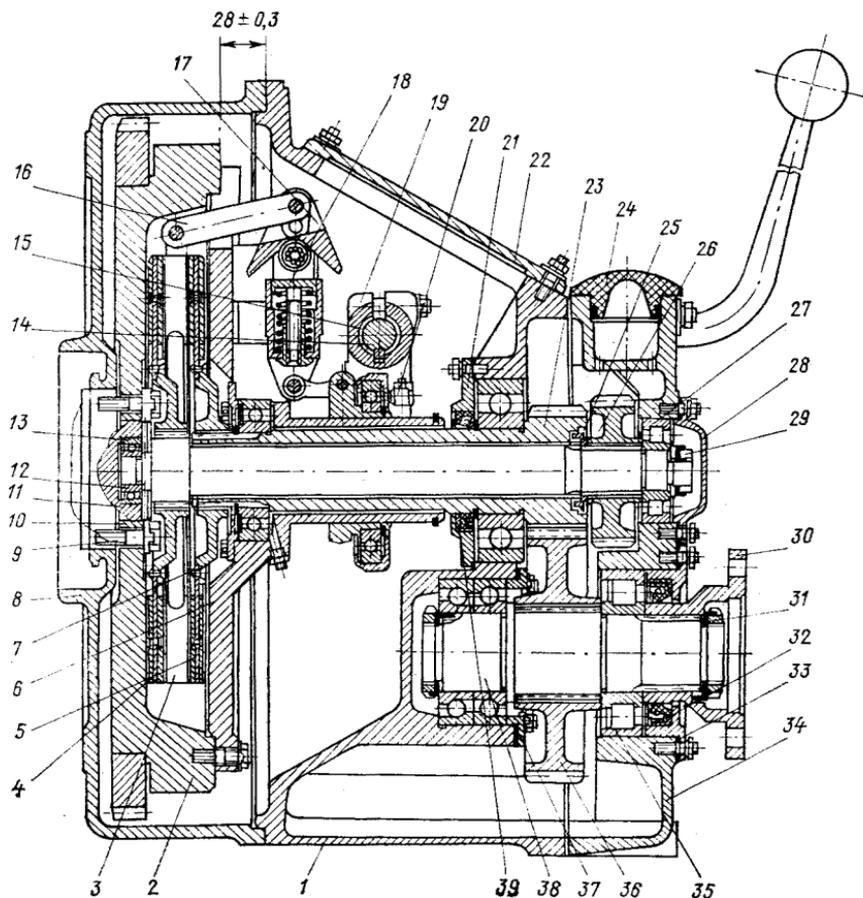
Продольный разрез реверсредуктора РРП-15.
